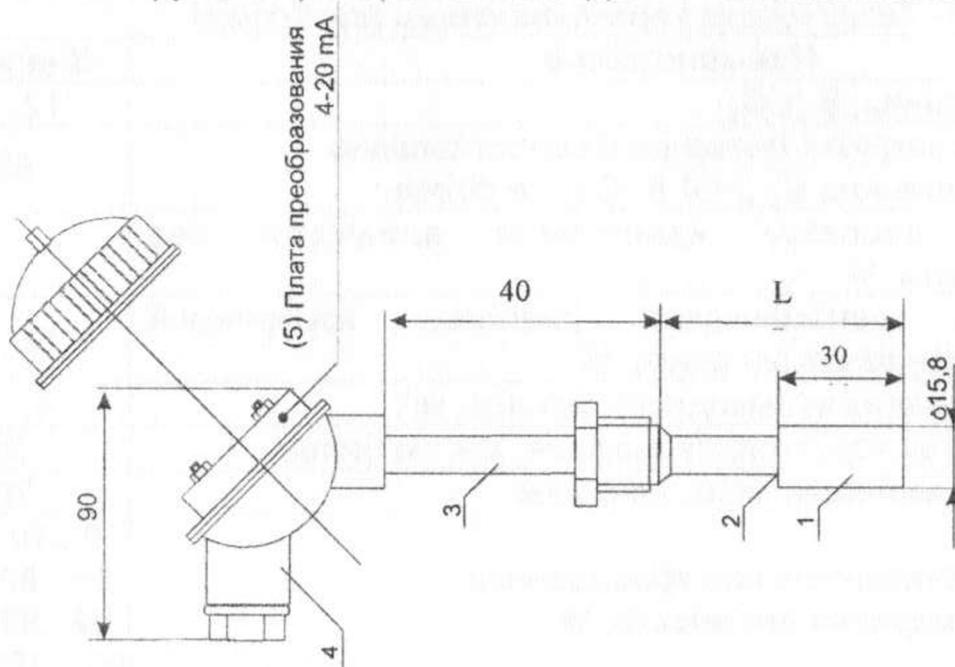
Конструкция преобразователя ДВ УТ-02
